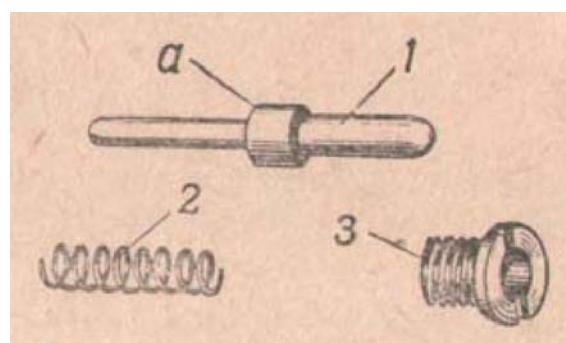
Детали инертного бойка: 1 - собственно боек; а - венчик для упора пружинки; 2 - возвратная пружинка; 3 - муфточка с резьбой для укрепления бойка с пружинкой в корпусе колодки
